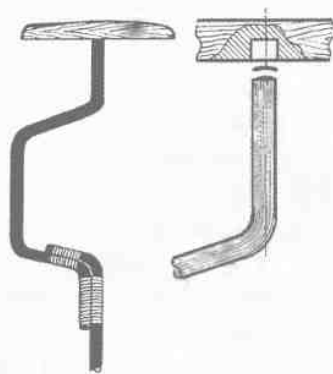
Самодельный коловорот для сверления глубоких отверстий
